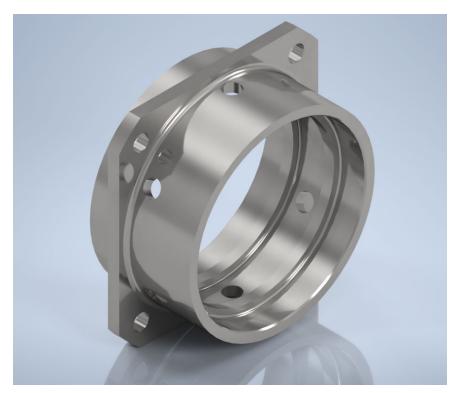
3Д модель детали «Втулка гидроцилиндра левая»
